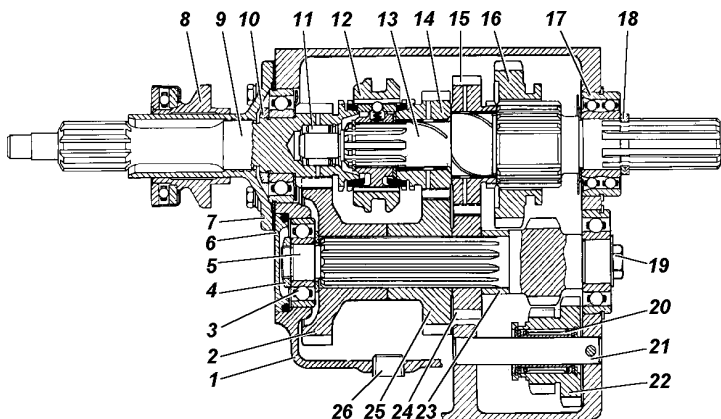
Вариант исполнения коробки передач с синхронизатором только для третьей и четвертой (прямой) передач:
